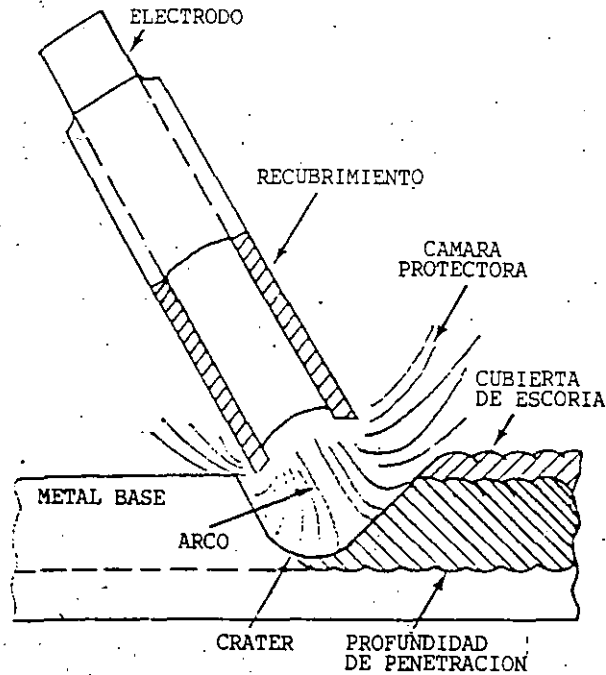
FIG. _____ SOLDADURA DE ARCO DE UN ELECTRODO REVESTIDO EN PROCESO.
